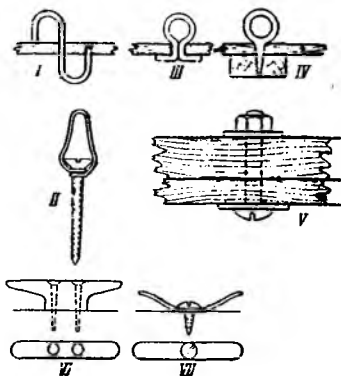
Мелкие детали: I — двойной обушок на люковую крышку; II — обушок из шнурка и проволоки; III — обушок из проволоки; IV — винтовой обушок; V — болтик подвижной мачтовой планки; VI — деревянная утка; VII — металлическая утка.
